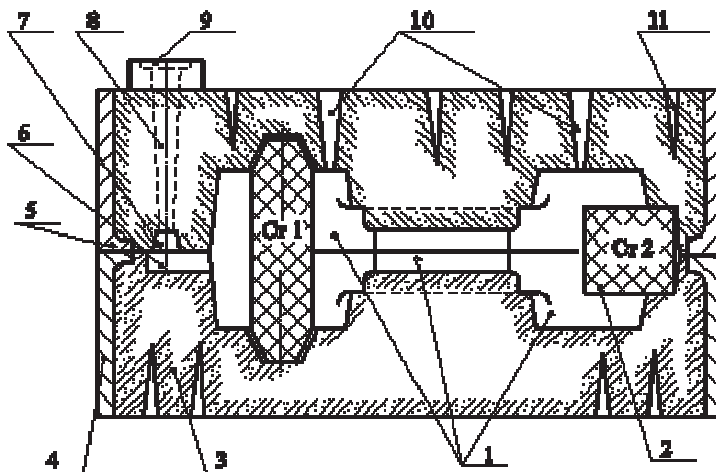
Схема литейной формы для получения отливки рычага: 1 – полость формы; 2 – стержни для получения отверстий в отливке; 3 – формочная песчано-глинистая смесь; 4 – нижняя опока; 5 – верхняя опока; 6–9 – литниковая система (предназначена для подачи жидкого металла в полость формы); 10 – выпоры; 11 – газоканалы
